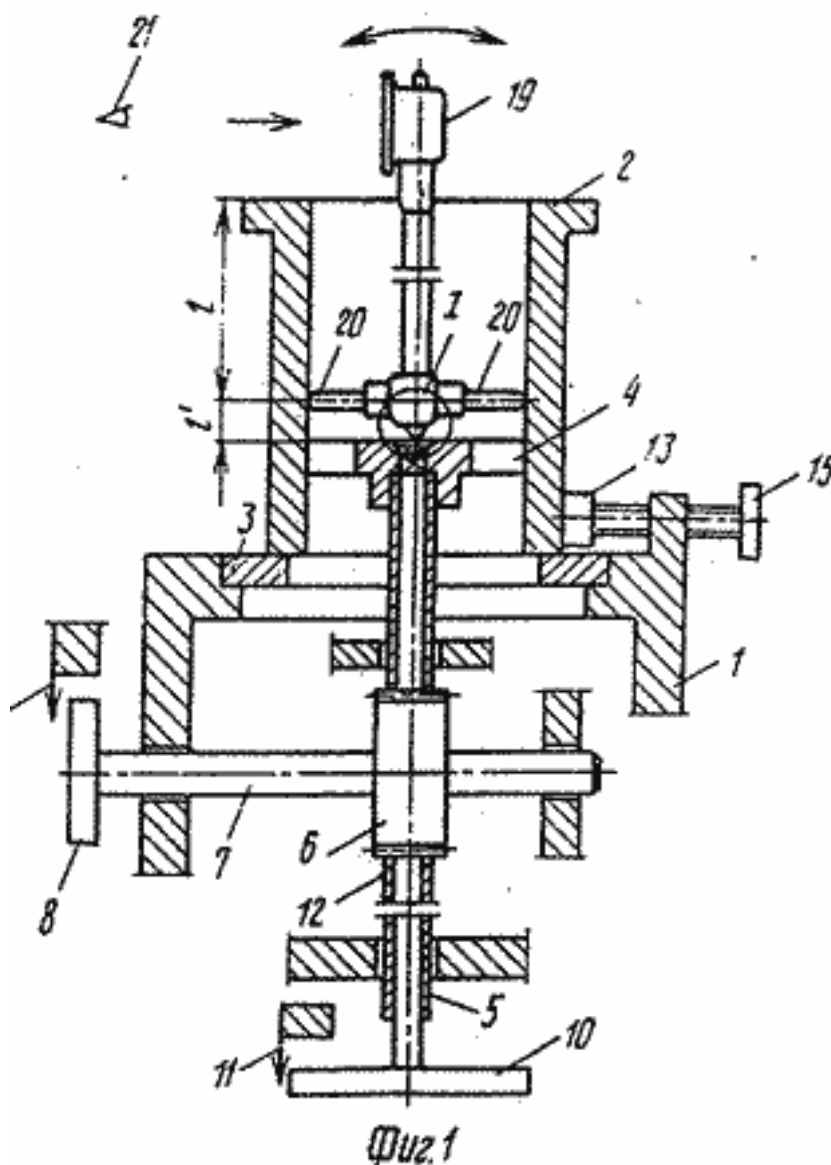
Пристрій для вимірювання внутрішнього діаметру деталей
